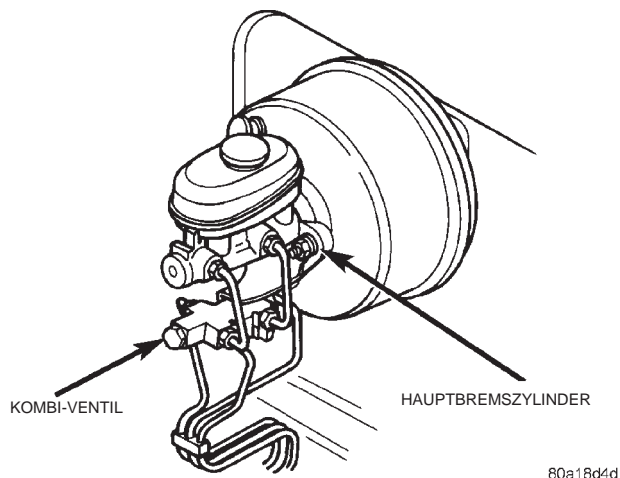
Kombi-Ventil und Hauptbremszylinder
